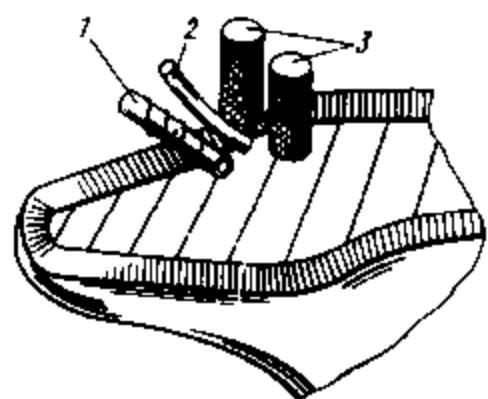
Схема исполнительных механизмов роликовой затяжной машины:
